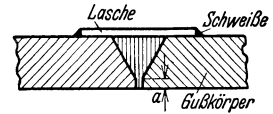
Gußschweiße mit Verstärkungslasche.
